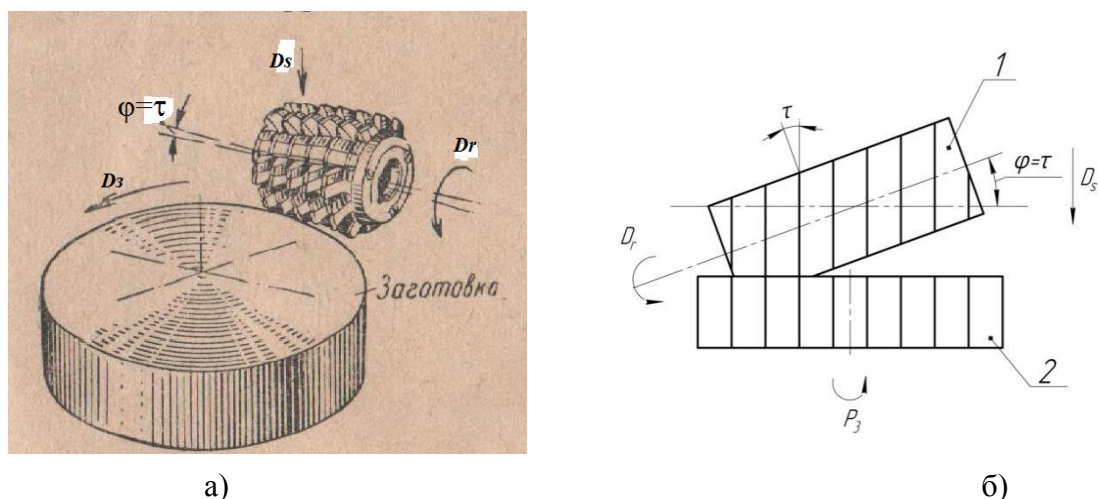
Основные движения (а) и схема нарезания (б) прямозубых колёс червячными фрезами
